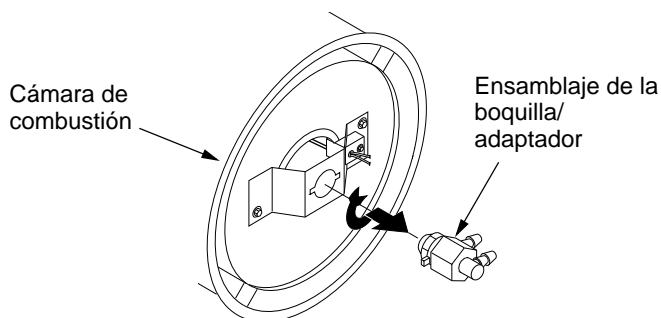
Desmontaje del ensamblaje de la boquilla/adaptador
